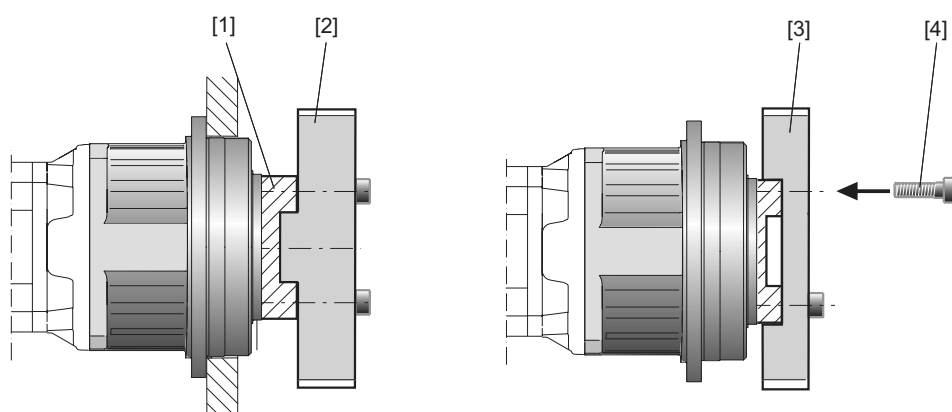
Exemplo de montagem para um bloco de flange PSBF..
